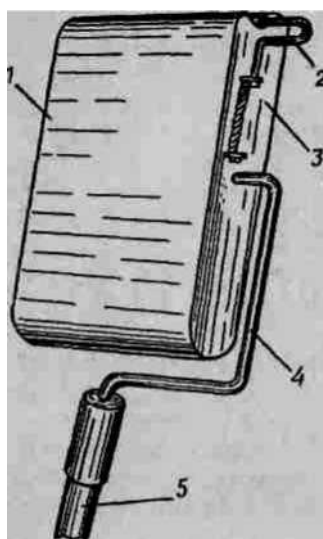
Пристрій для очищення поверхні шліфувальною шкуркою: 1 - шліфувальна шкурка; 2 - пружинний затискач; 3 — корпус; 4—вилка; 5 —ручка
